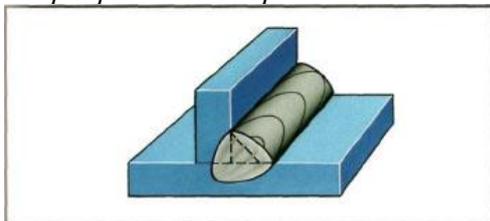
Чрезмерная асимметрия сварного шва (Код дефекта: 512)
